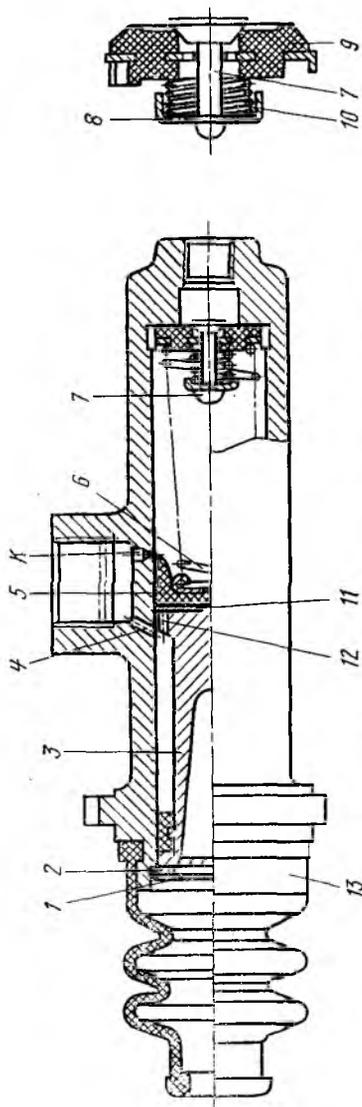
Главный тормозной цилиндр погрузчика Ф8.ЕУ20.33:
